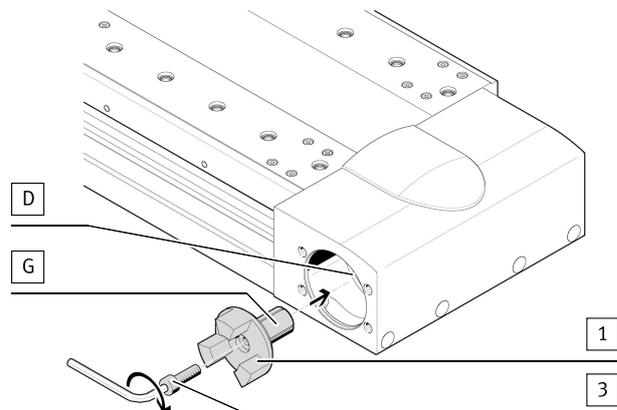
Крепление ступицы муфты, на стороне координатного привода
